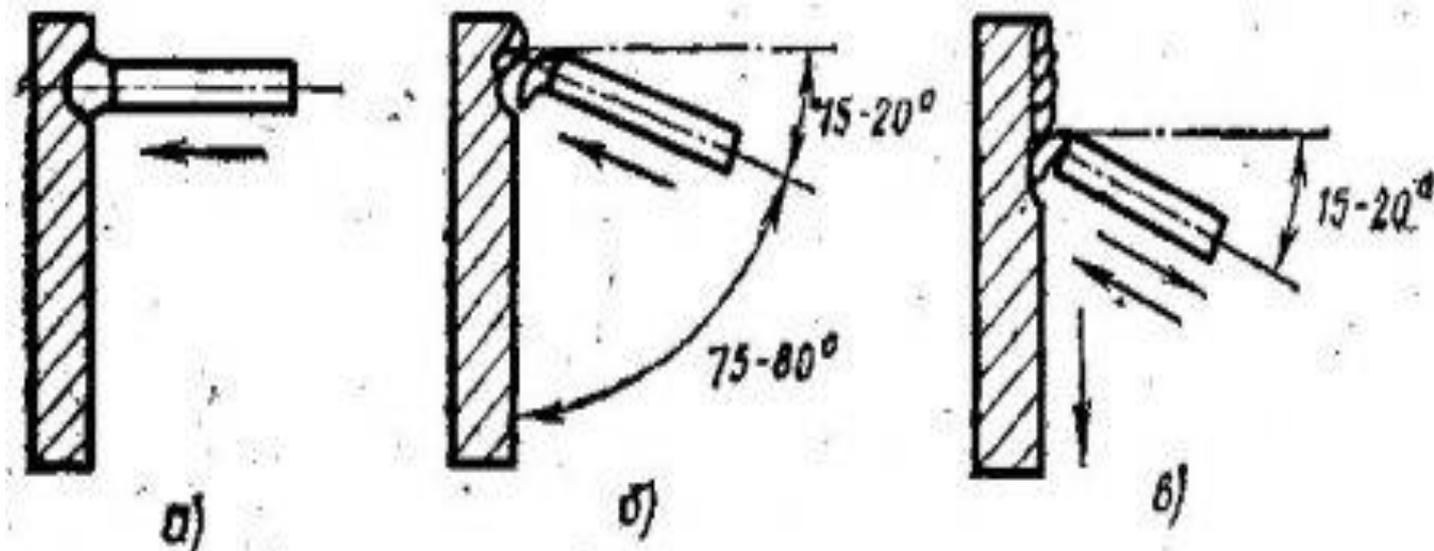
Схема техники сварки (наплавки) на спуск:
